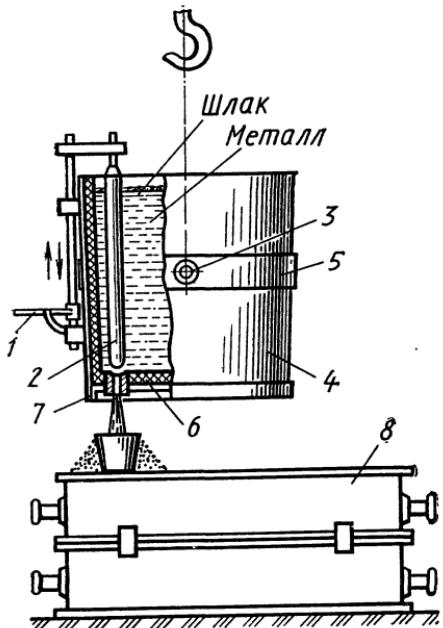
Схема заливки формы сталью из стопорного ковша:
